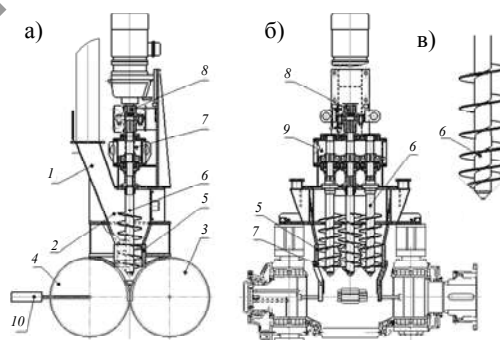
Схема валкового пресса: общий вид (а); вид сбоку (б); шнек с переменным шагом винтовой навивки (в)
